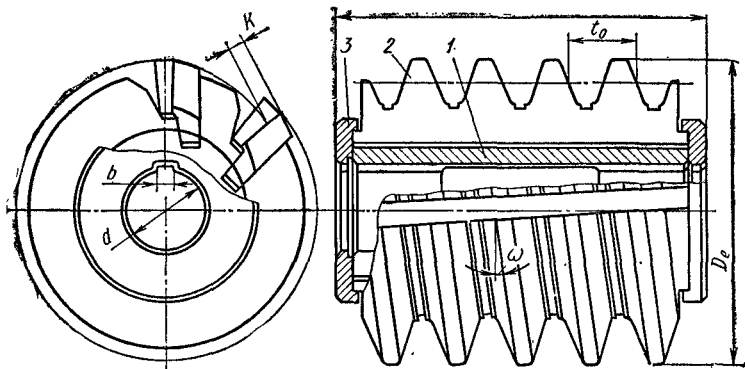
Червячные фрезы со вставными гребенками конструкции завода «Фрезер»
